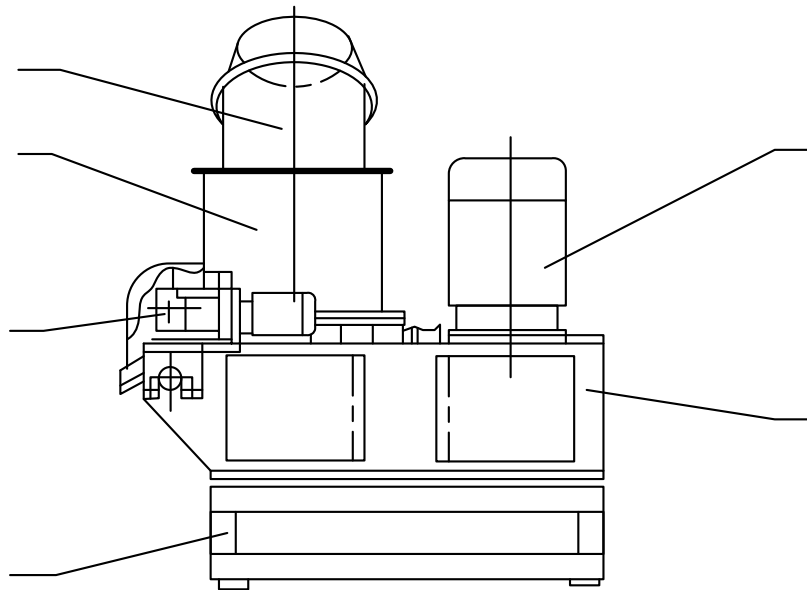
Агрегат мийно-різальний: 1 - каркас підставки; 2 – станина; 3 - електродвигун; 4 – корпус; 5 - завантажувальний бункер; 6 - редуктор
